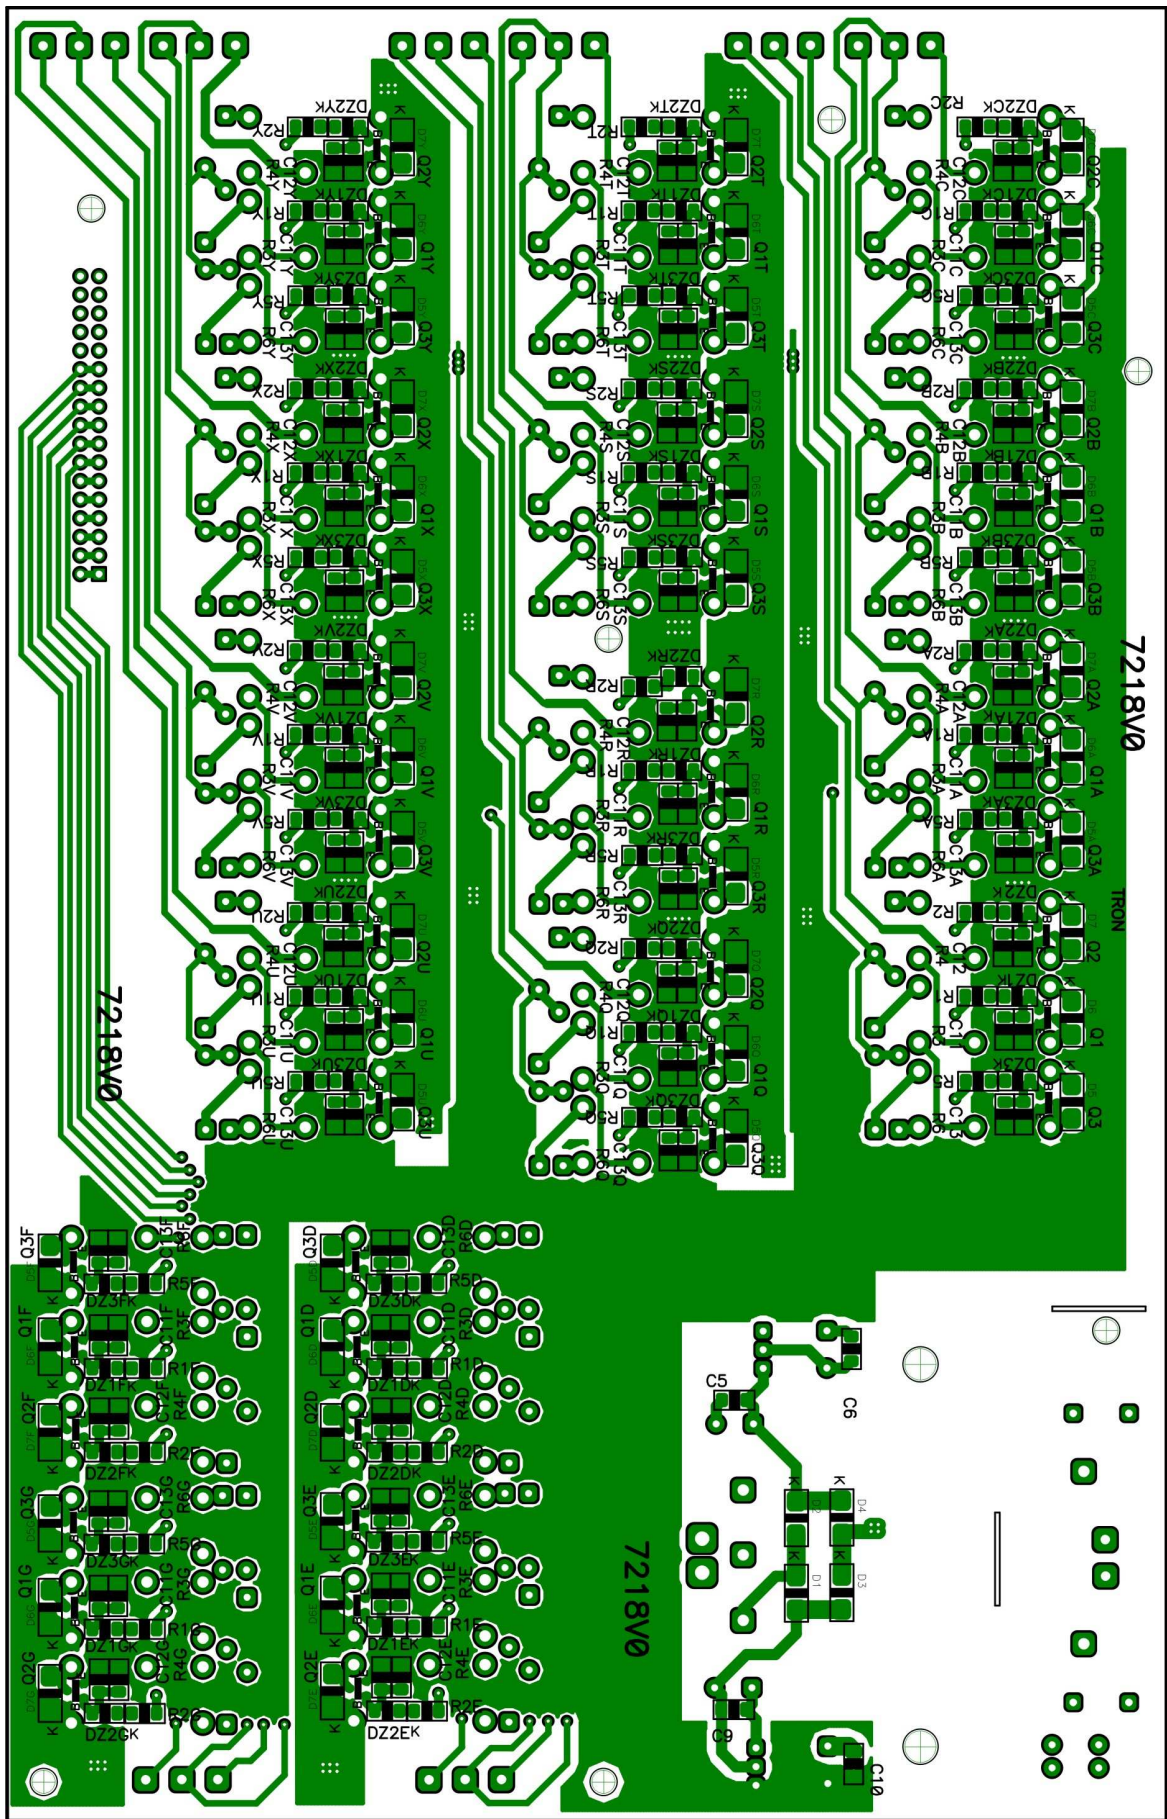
Placa Filha de Nível - Face da Solda e dos Componentes SMD
